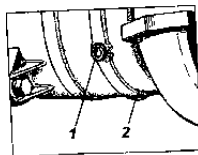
Пробки коробки передач: 1 -контрольная пробка; 2 сливная пробка
